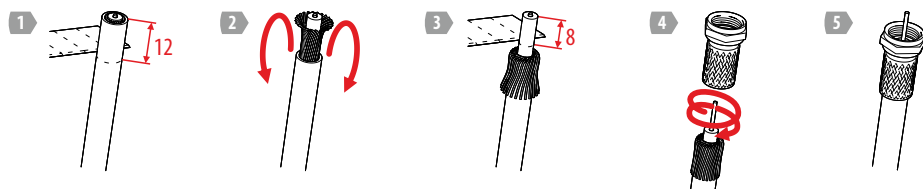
Разделка коаксиального кабеля и установка F-разъема
